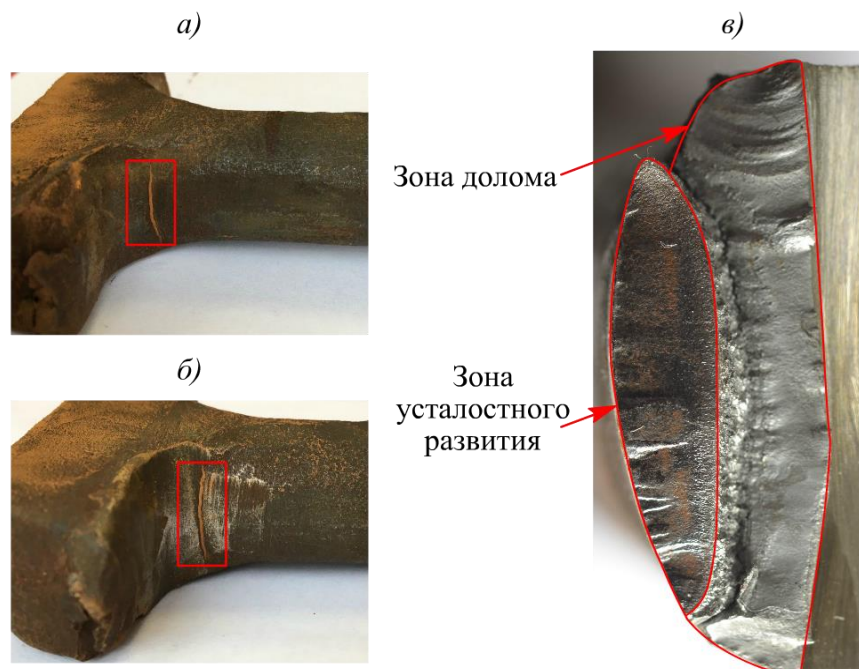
Исследуемый образец маятниковой подвески с обнаруженным дефектом: магнитная индикация до зачистки (а), магнитная индикация после зачистки (б), излом детали со стороны стержня (в)
